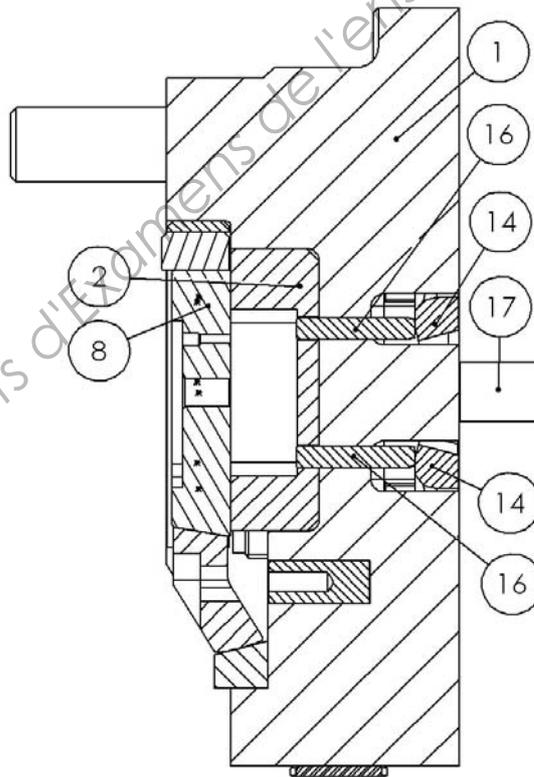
Coupe longitudinale LL (repérée sur figure 2)
